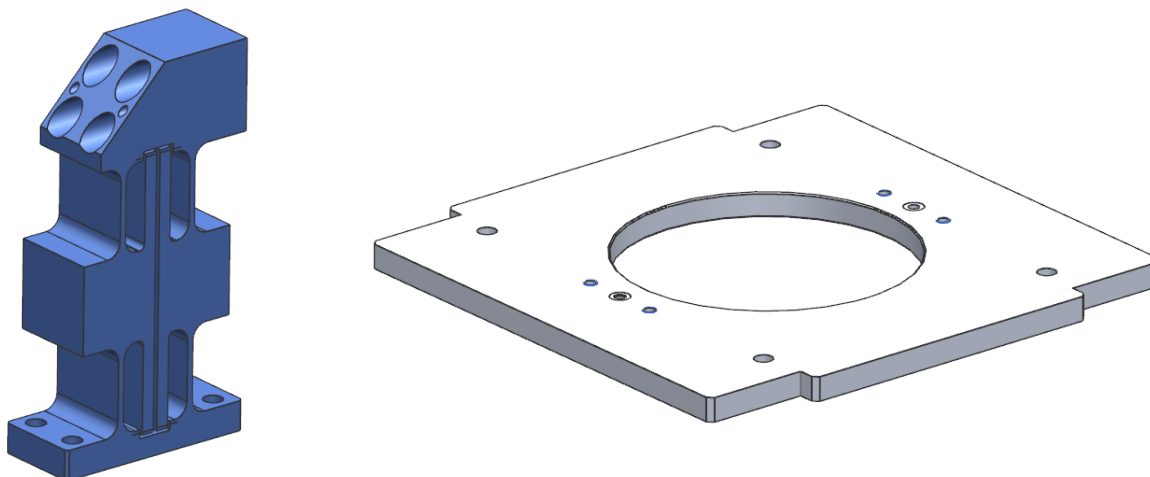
Traverse flexible (à gauche) et platine FS croix de malte (à droite)
